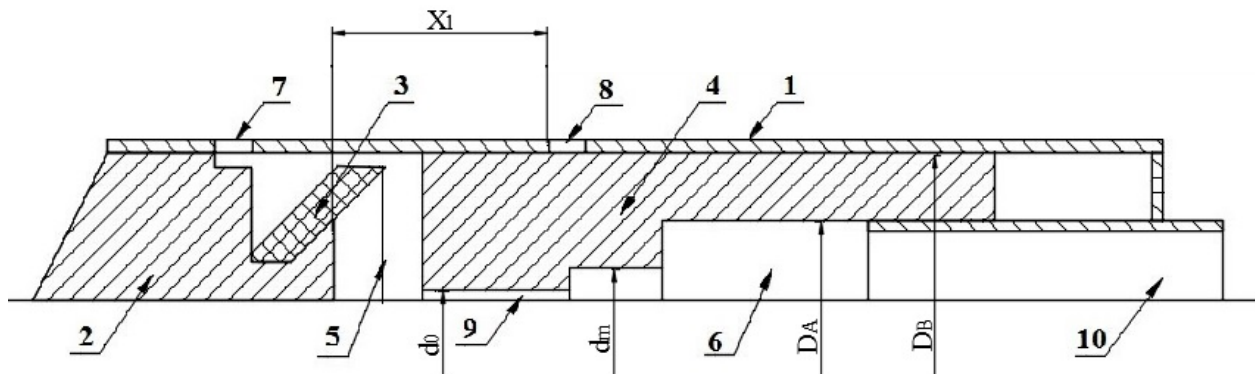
Принципиальная схема ударной машины: 1 — корпус; 2 — наковальня; 3 — клапан; 4 — боек; 5 — камера обратного хода; 6 — камера прямого хода; 7 — первое выхлопное отверстие; 8 — второе выхлопное отверстие; 9 — межкамерный дроссель; 10 — подача воздуха
